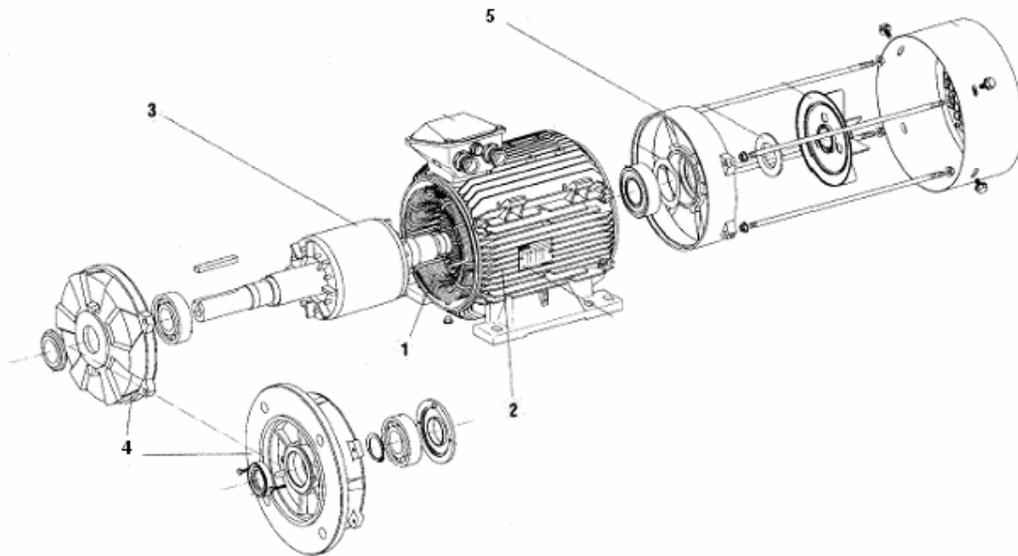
Machine asynchrone à cage d'écureuil SIEMENS
